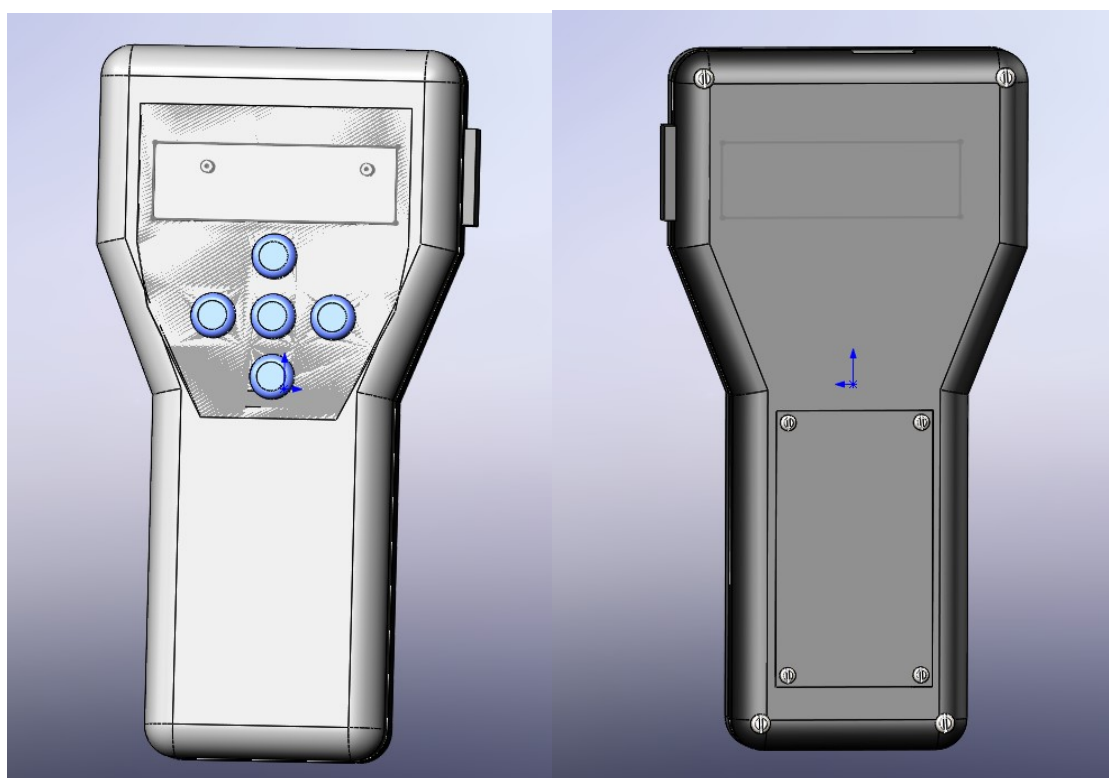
Твердотельная модель измерителя напряжений в арматуре
